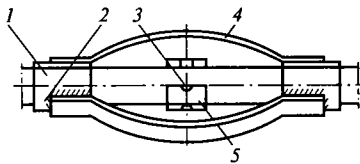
Центрирующий фонарь (центратор) конструкции ГрозНИИ: 1 — обсадная труба; 2 — кольцо; 3 — отверстия для сварки; 4 — планки; 5 — упорное кольцо
